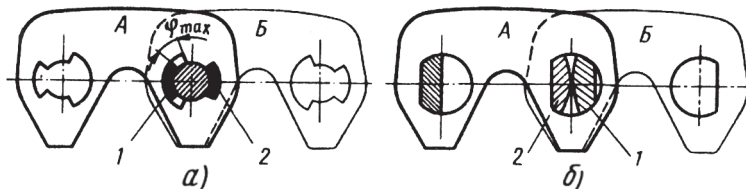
Зубчатые цепи: конструкция шарниров
